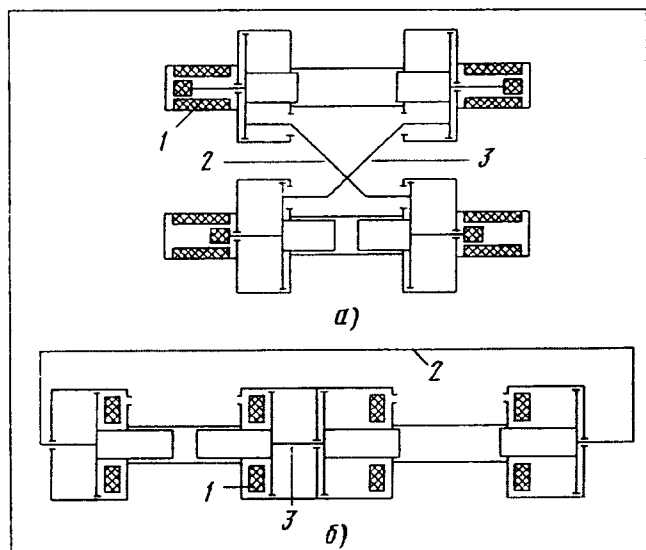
Схема двухцилиндрового модульного двигателя с механической связью модулей, параллельным (а) и соосным (б) расположением цилиндров
